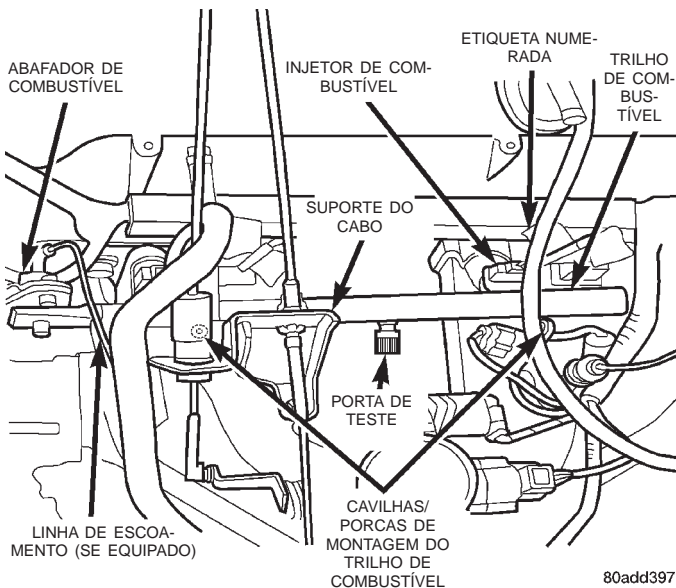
Montagem do Trilho de Combustível— Motor 2.5L
